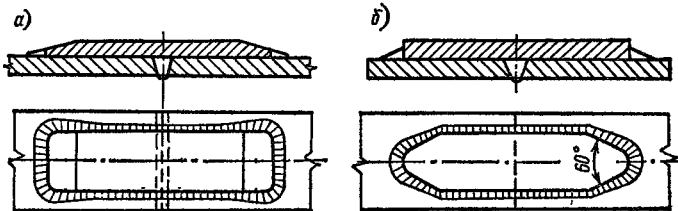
Сварные соединения на накладках со скосами: *а* — по высоте; *б* — в плане
